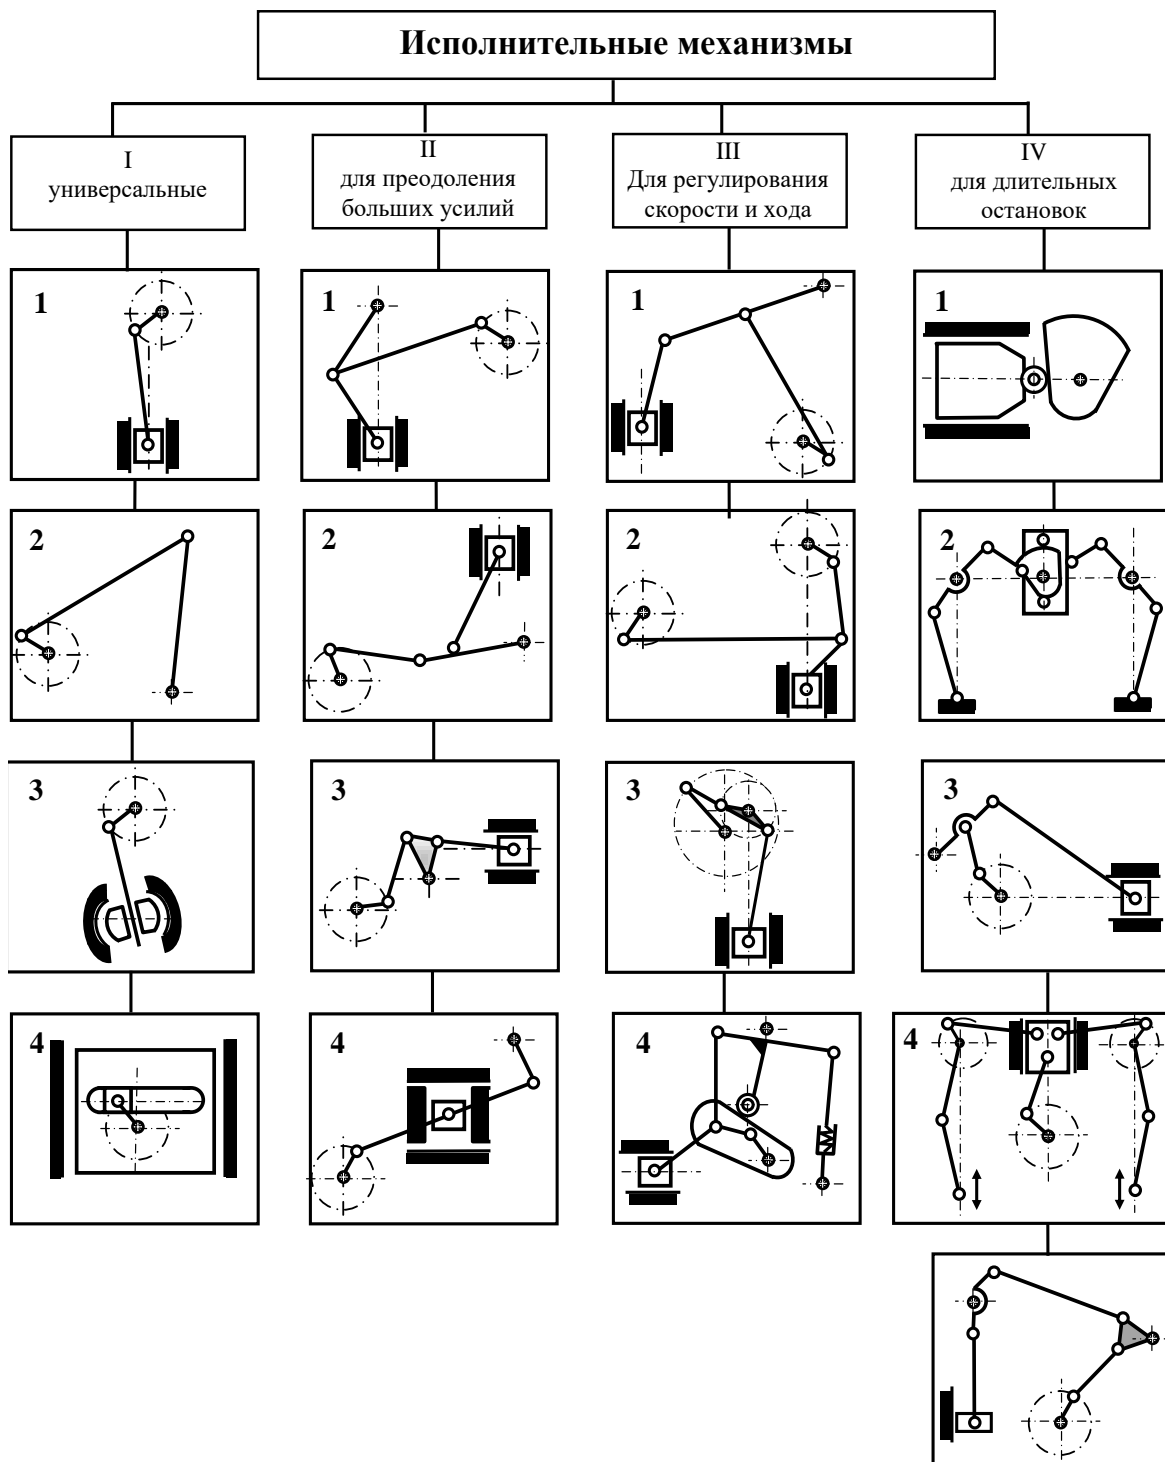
Исполнительные механизмы кривошипных прессов
